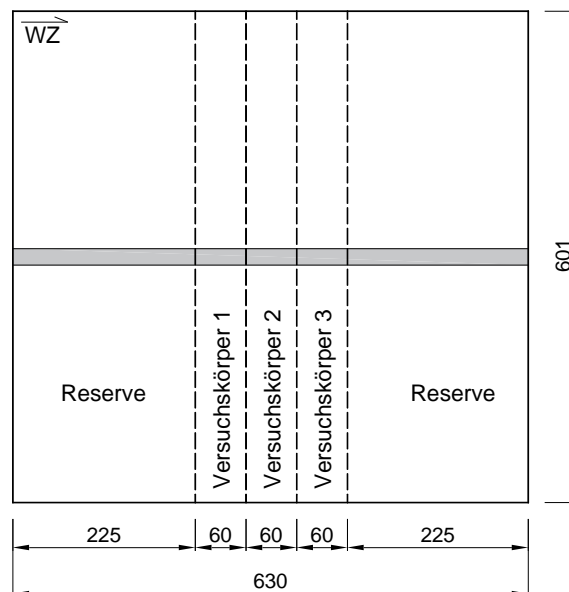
Geschweißtes Blech zur Entnahme der Zugproben
